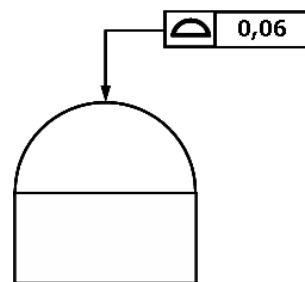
Indicação de tolerância de forma de uma superfície qualquer em desenho técnico
